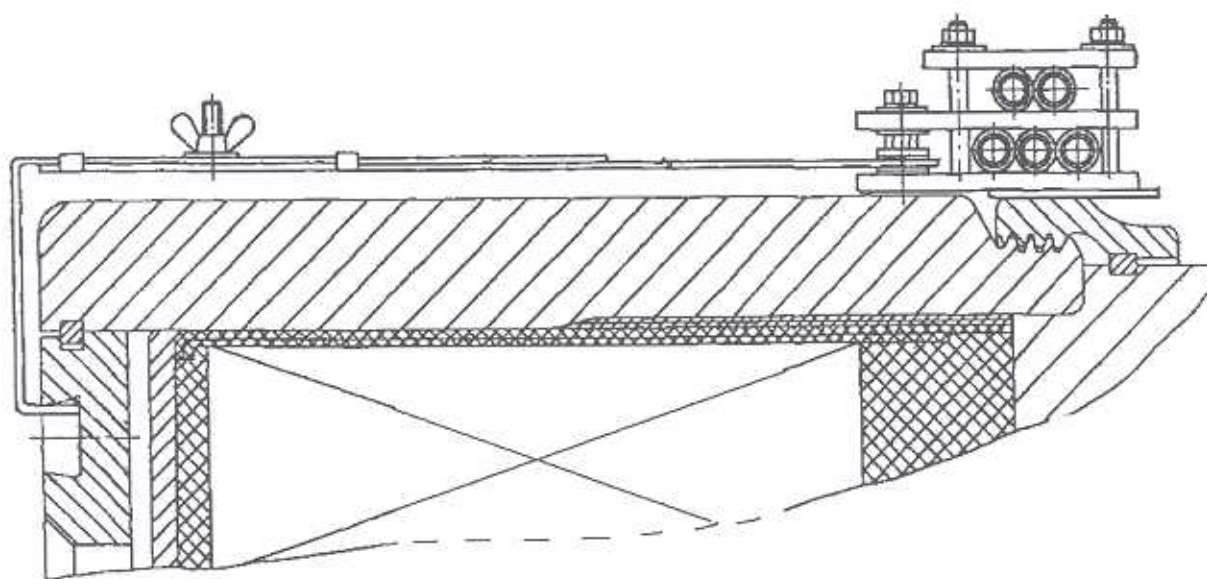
Установка индуктора для нагрева гайки крепления бандажного кольца
